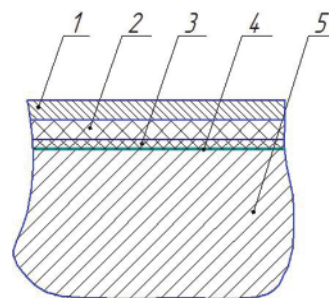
Корпус газогенерирующего устройства в разрезе: 1 – корпус; 2 – теплозащитное покрытие; 3 – защитно-крепящий слой с капроновой тканью; 4 – крепящий состав; 5 – твердое топливо
